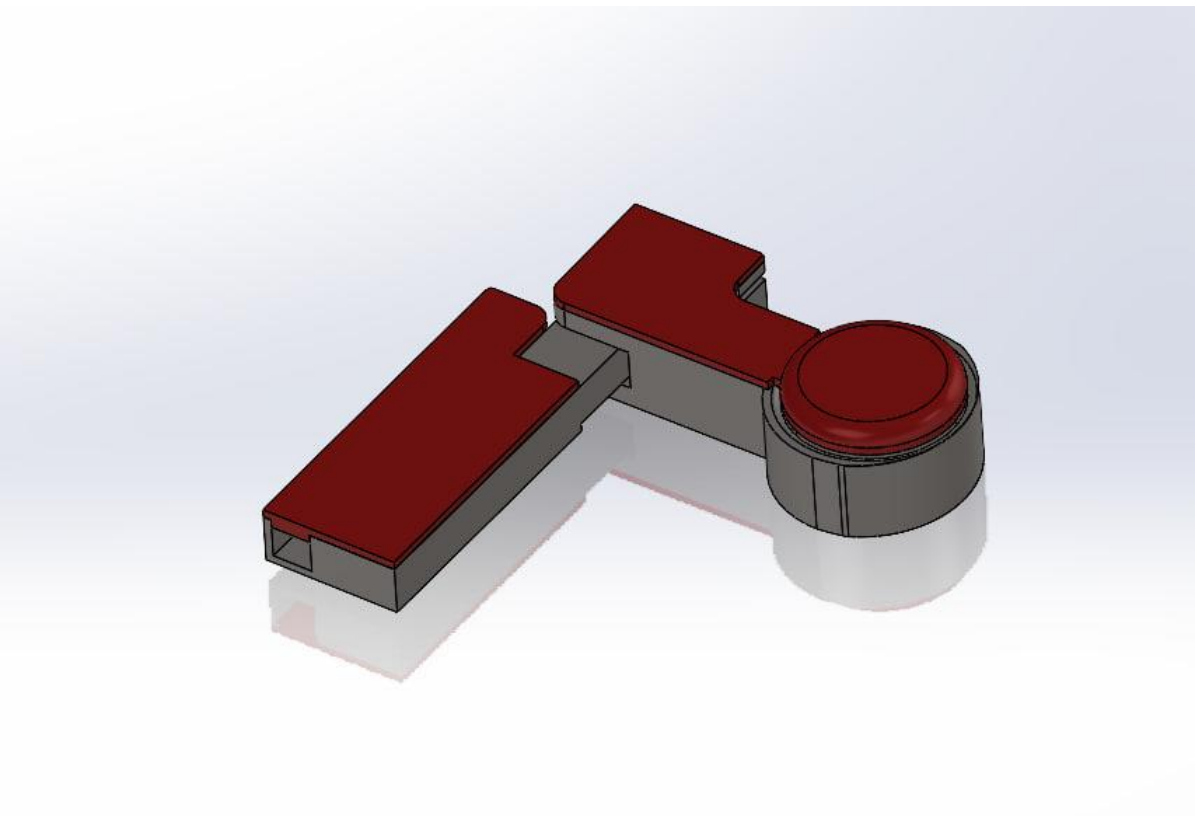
Корпус гнатодинамометра для измерения нагрузки отдельных зубов (вид сбоку)
